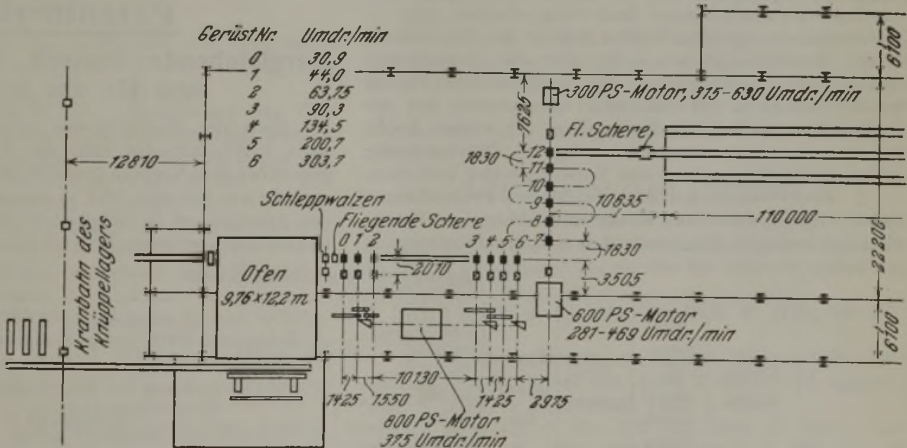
Feineisenwalzwerk der Donner Steel Co., Buffalo.
